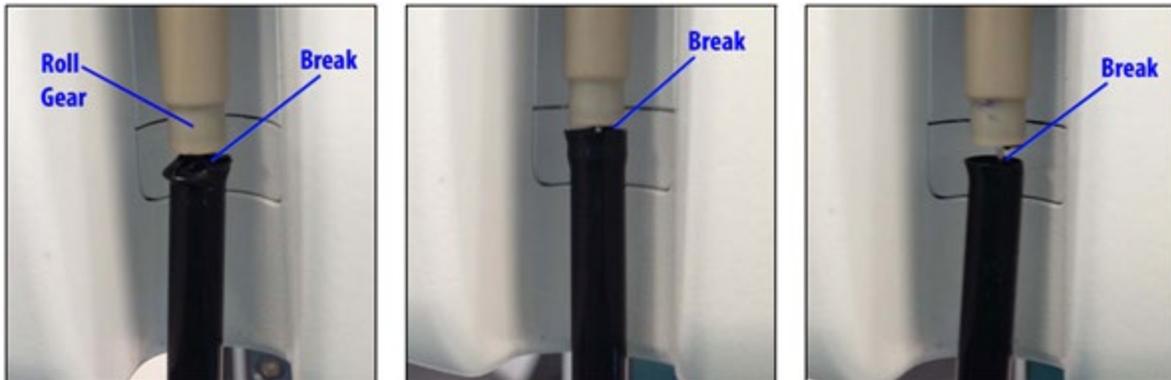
roll gear 및 instrument shaft 접합부의 brake 의 예
